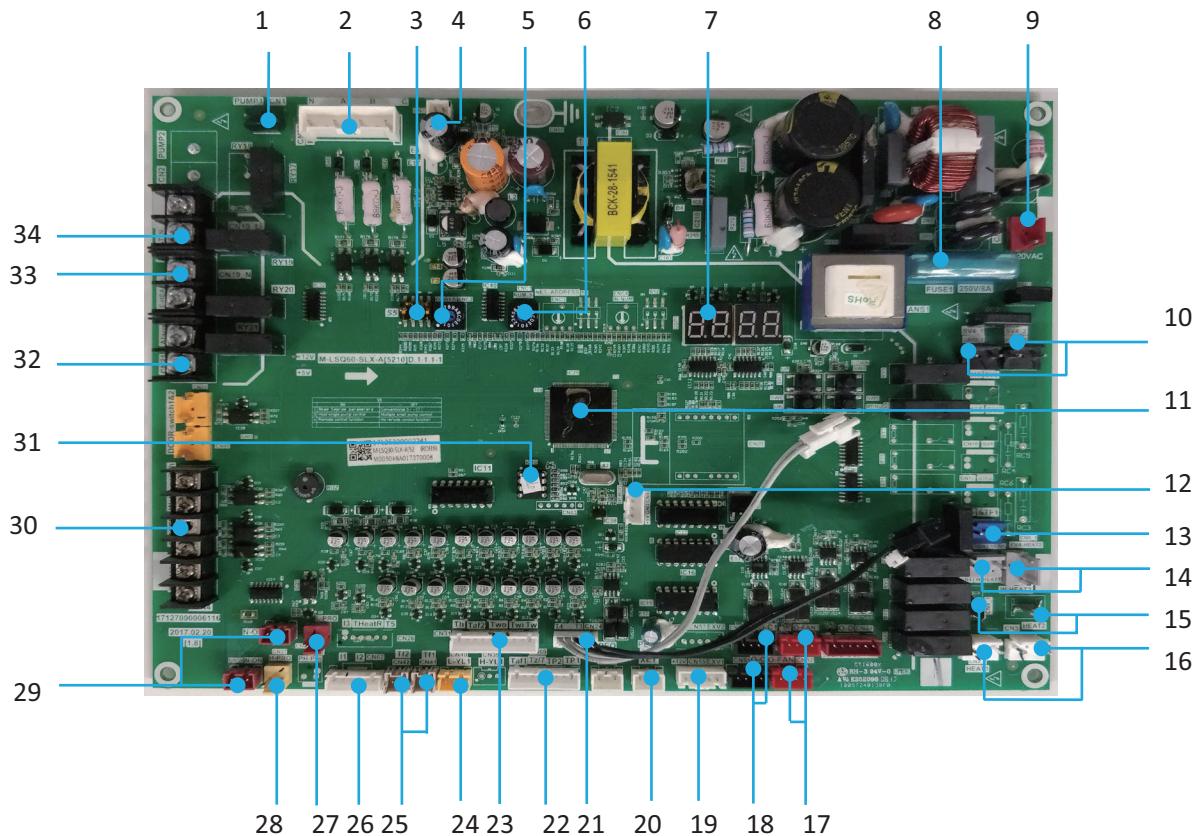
PCB principale dell'unità KEM-90 DNS3
